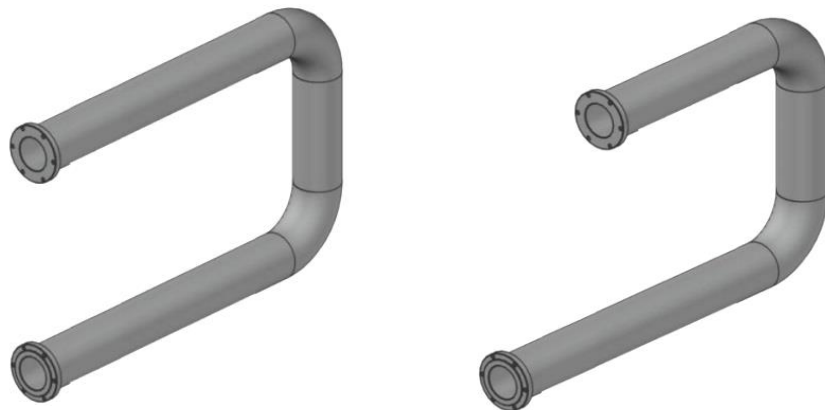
Варіанти трубопроводу без розгалужень й арматури
